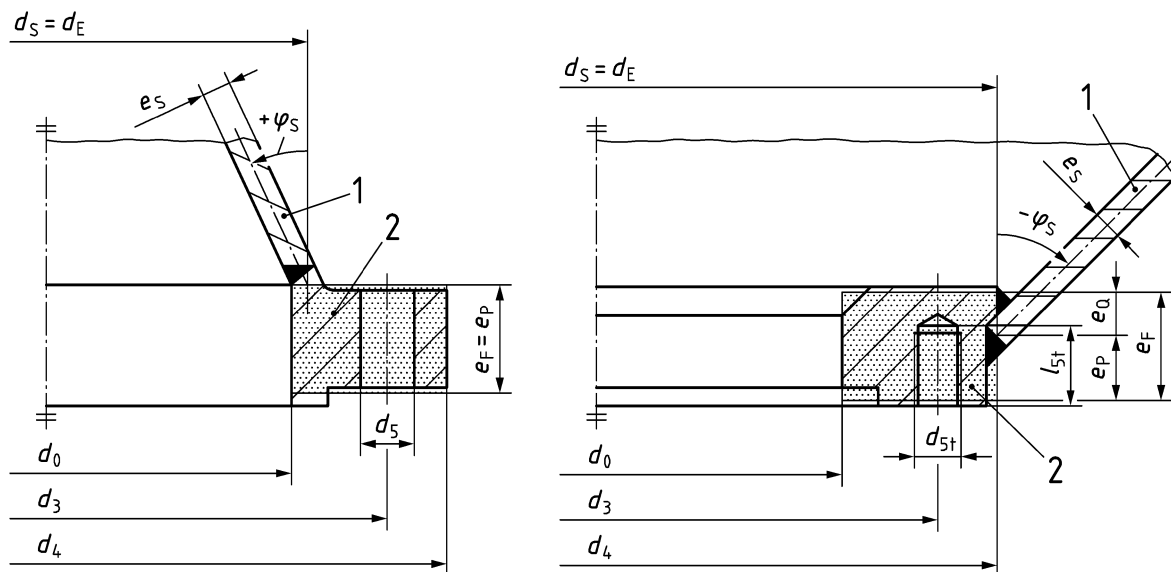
Vorschweißflansche mit Zylinderschalen (Beispiel 1)
